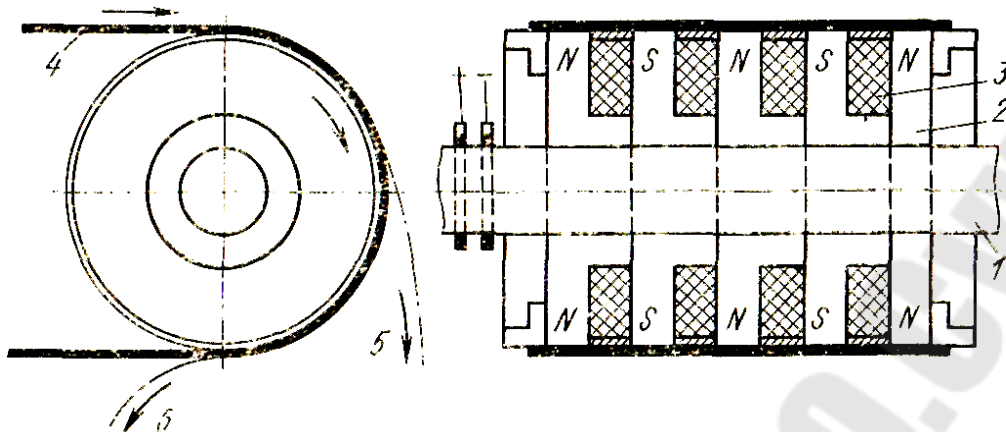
Шкивной железоотделитель: 1- вал; 2- сердечник; 3- катушки; 4- лента конвейера; 5- немагнитный материал; 6- магнитные включения
